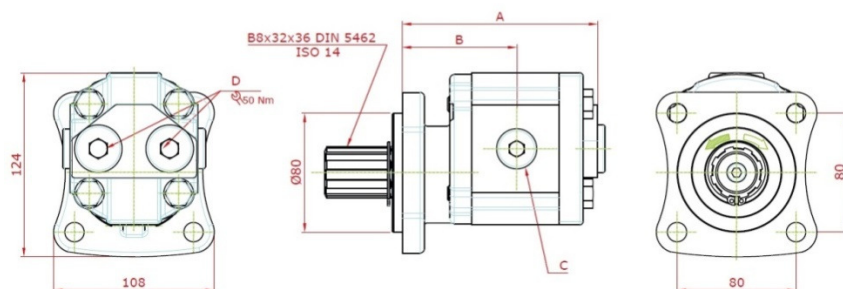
Dimensiones de la bomba hidráulica Bezares BEA 17 (5060906)
